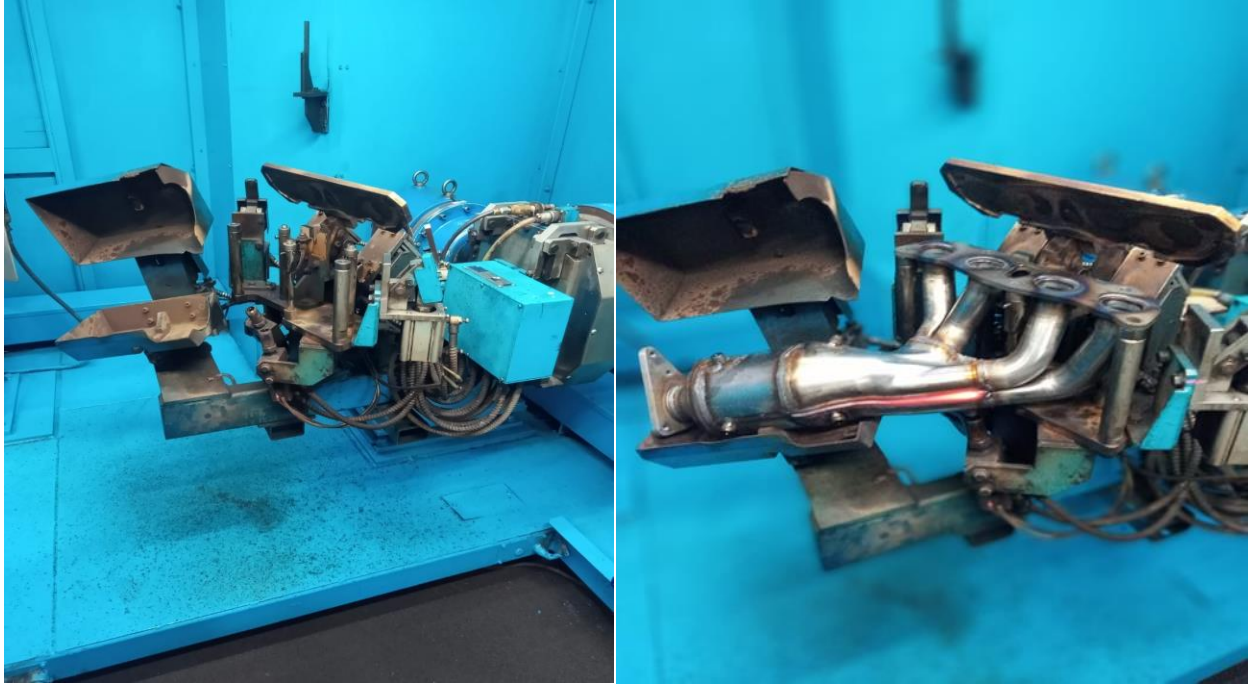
Imágenes referentes a la cabina #5 (lado A) de soldadura.
